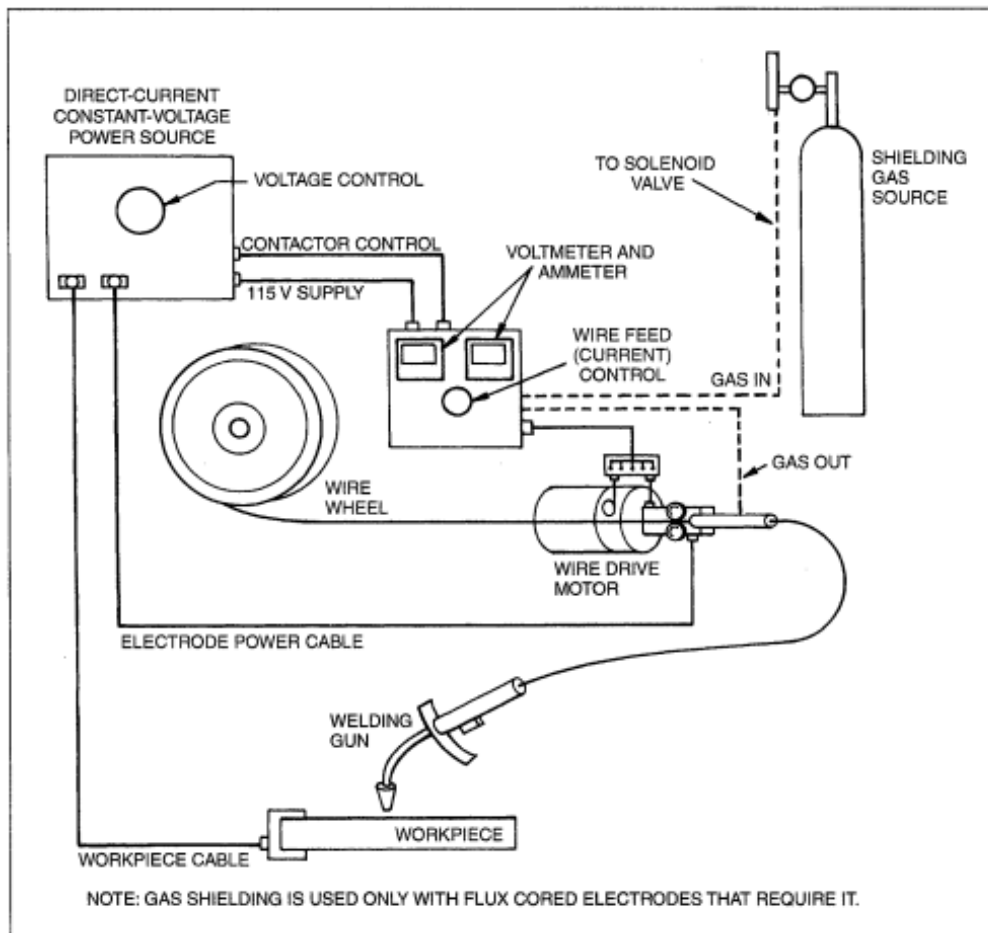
Equipos empleados para soldadura FCAW: alimentador con motor, fuente de poder, gases de aporte, antorcha.
